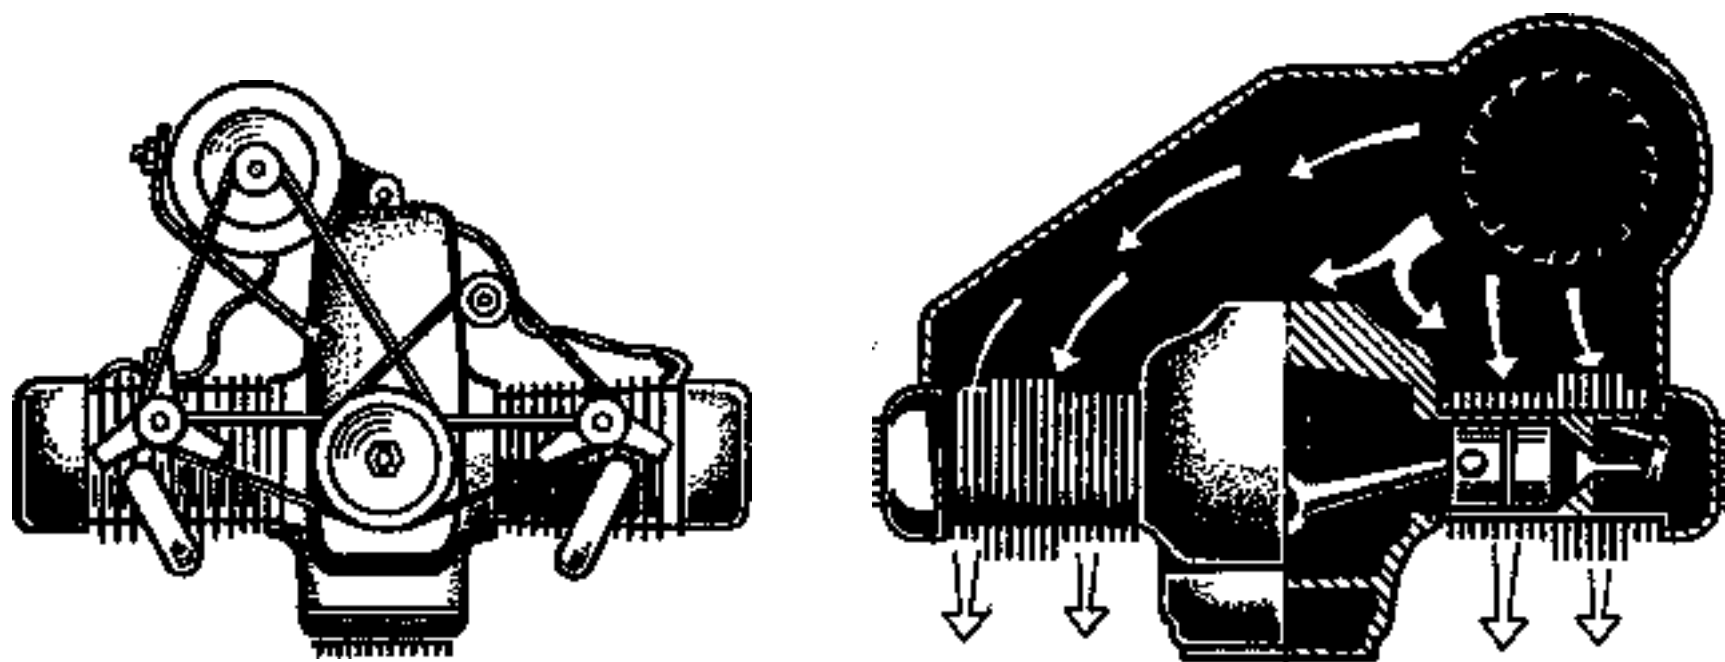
Схема устройства принудительного охлаждения оппозитного двигателя:
